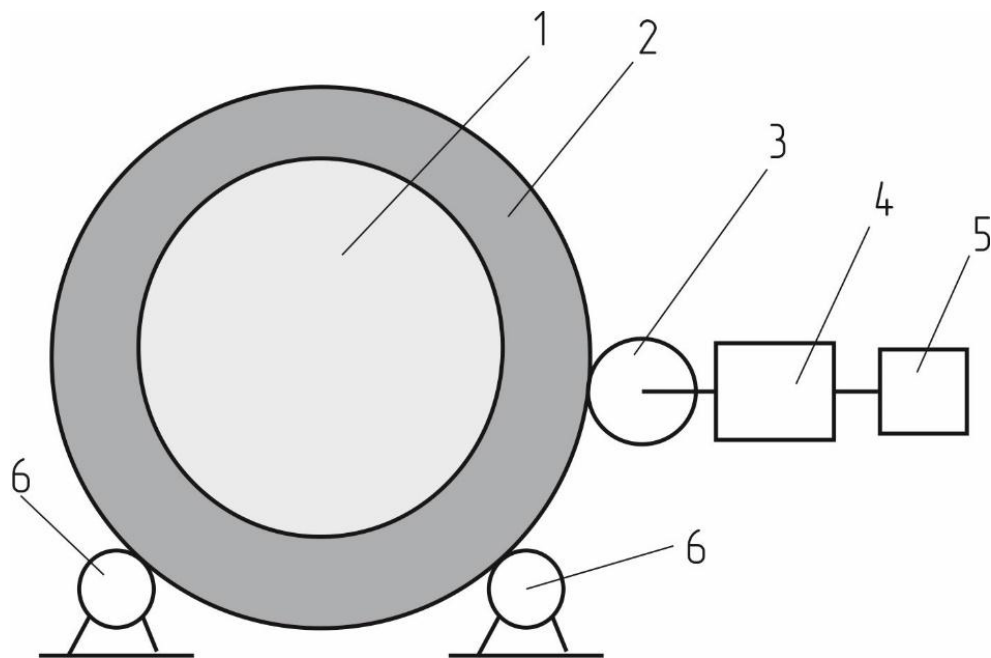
Схема приводу змішувача в дію: 1 – бункер змішувача; 2 - зубчате вінець; 3 – зубчате колесо; 4 – редуктор; 5 – електродвигун
